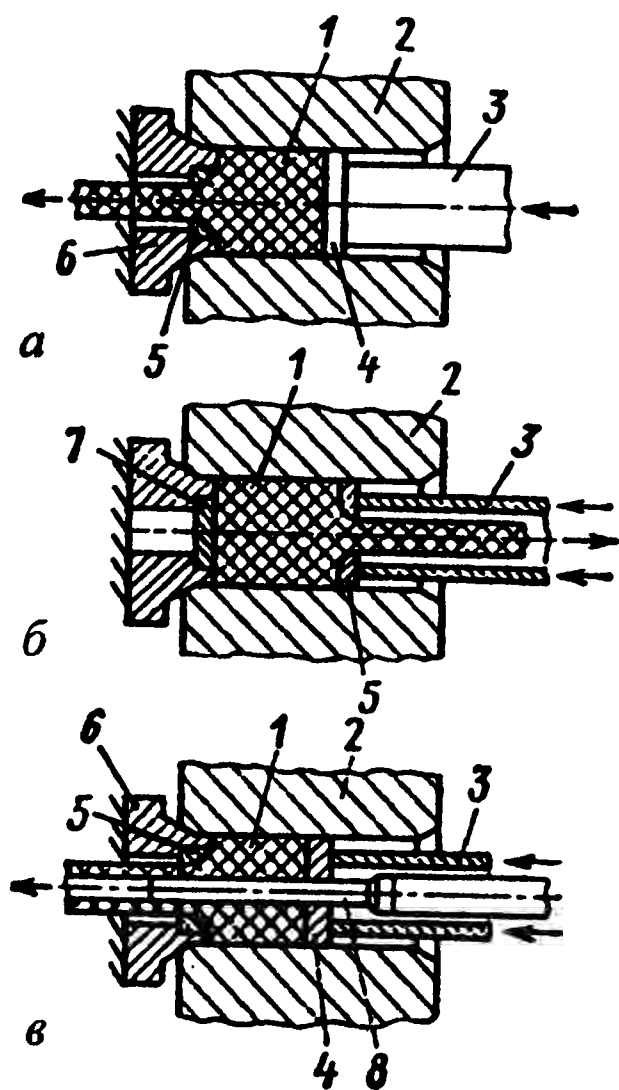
Схемы прессования прямого (*а*), обратного (*б*) и получение пустотелого (*в*) профиля на примере трубы: *1* — заготовка; *2* — контейнер; *3* — пуансон; *4* — пресс-шайба; *5* — матрица; *6* — матрица-держатель; *7* — заглушка; *8* — игла
